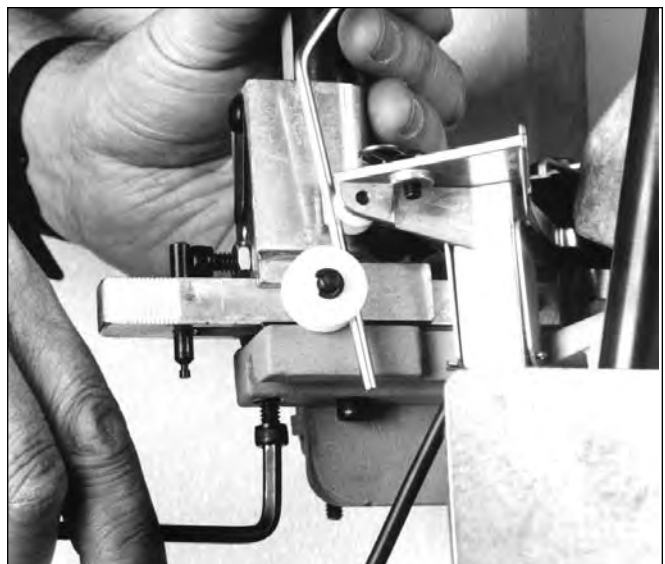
Entfernen des Zündhütchenzuführungskörpers zum Wechseln der Zündhütchenzuführungen. Vorsicht! Ziehen Sie diesen Bolzen (#14014) nicht zu fest.
